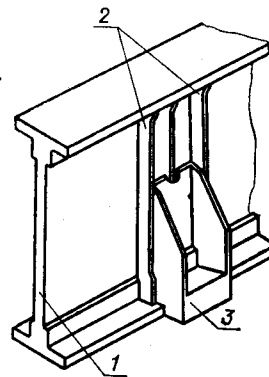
Пример сборки по базовым поверхностям деталей:
